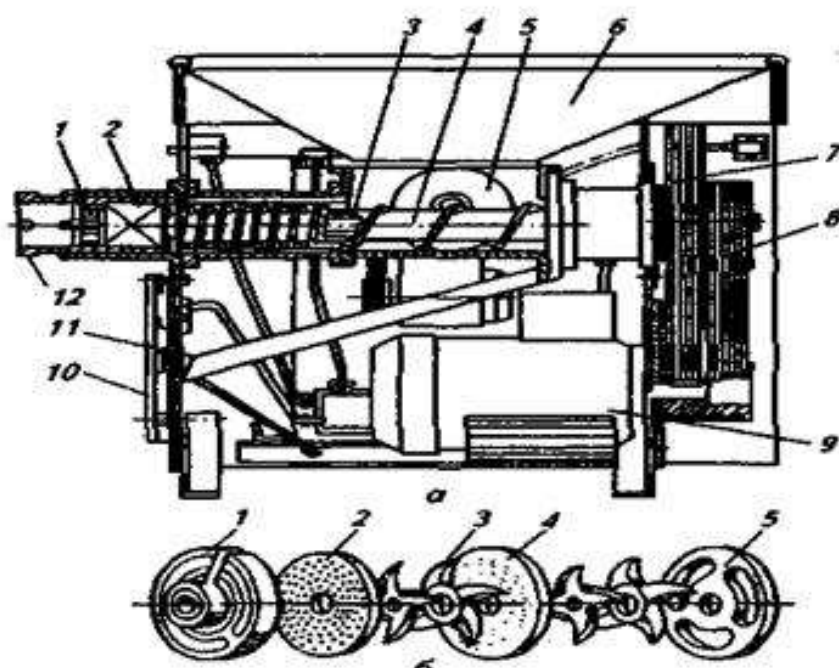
Вовчок К7-ФВП-160-2: а - схема подрібнювача (вовчок): 1 - підпирні решітки; 2 - ріжучий механізм; 3 - ножовий вал; 4 - робочий шнек; 5 - одновиткова лопать; 6- бункера; 7- клинопасова передача робочого шнека; 8- клинопасова передача ножового валу; 9 - електродвигун; 10- майданчик для санобробки; 11 -желоб; 12- трубчаста насадка;
